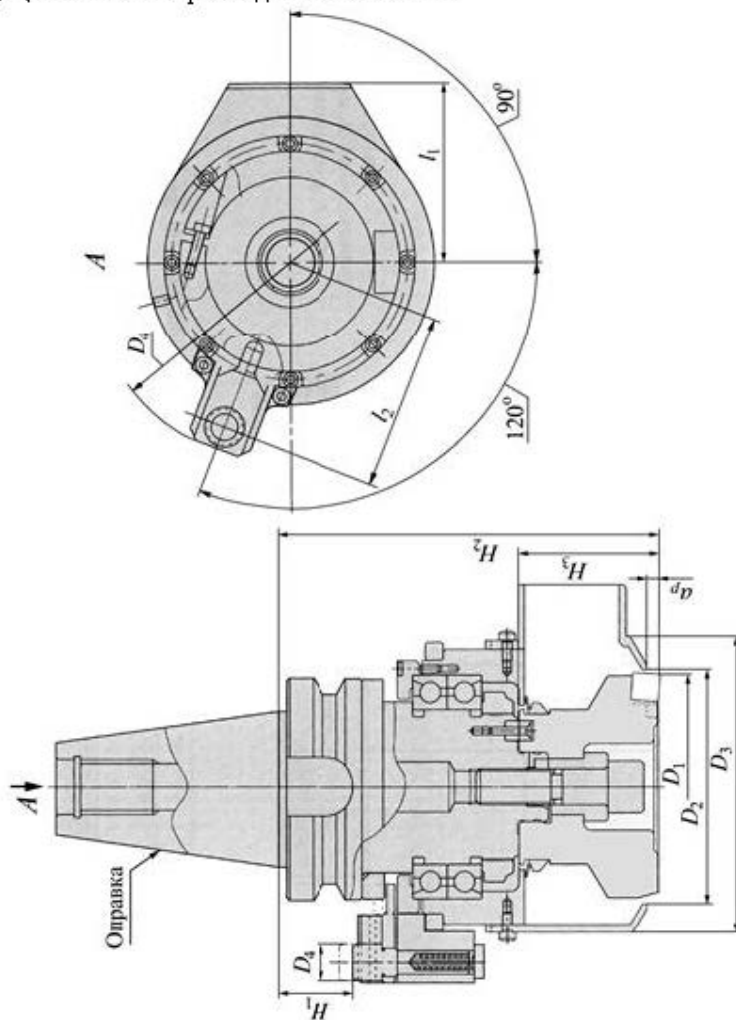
Специальная оправка для торцовых фрез для центробежного отвода стружки
